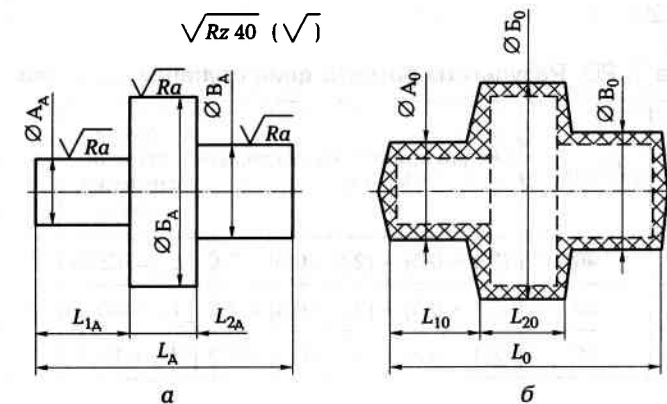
Деталь — вал (а) и штампованная заготовка (б) для вала
